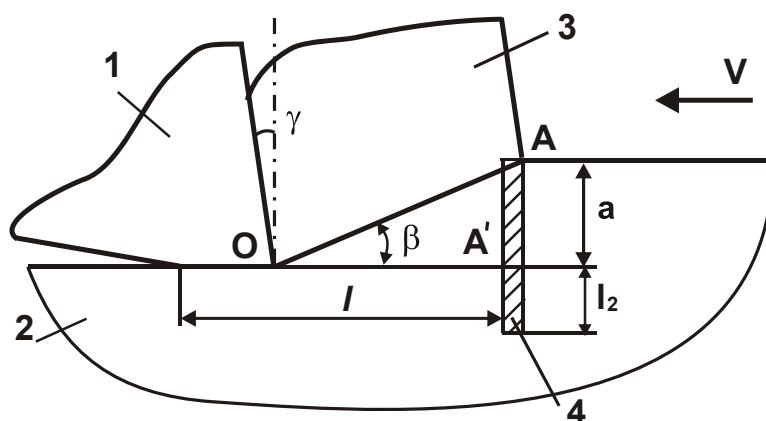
Расчетная схема параметров процесса точения: 1 – резец; 2 – обрабатываемый материал; 3 – образующаяся стружка; 4 – адиабатический стержень
